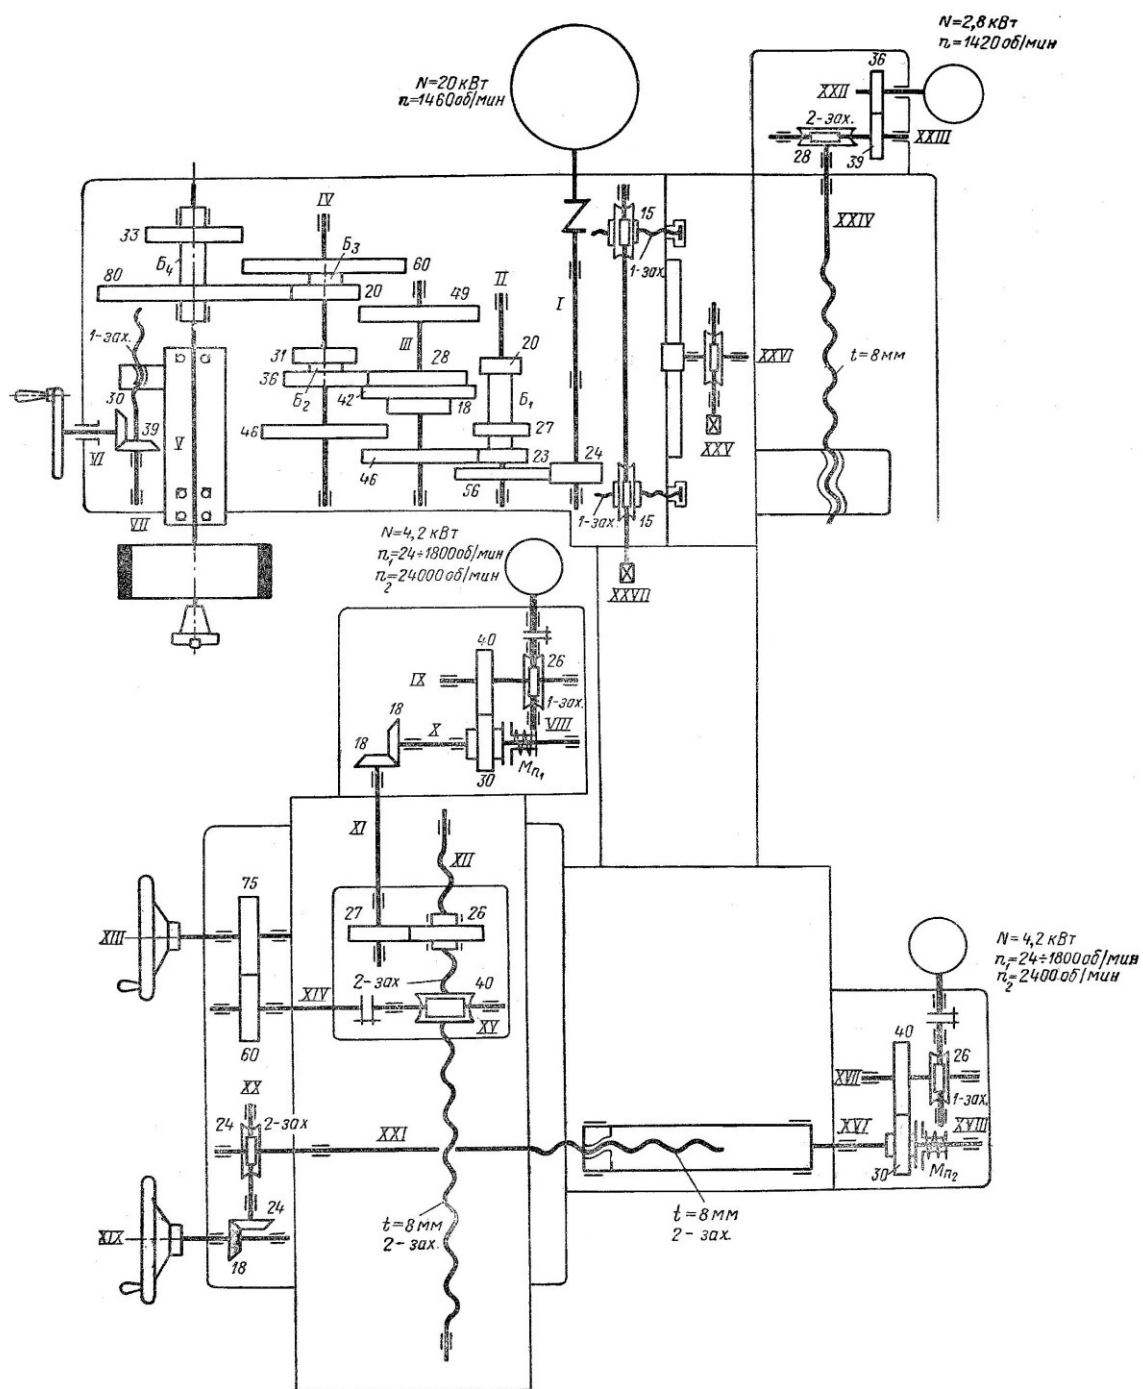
Бесконсольный вертикально-фрезерный станок мод. 656П
